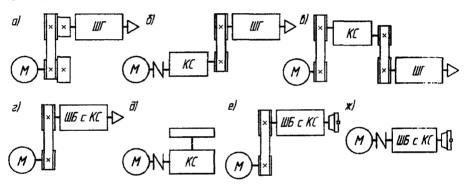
Рисунок I — Типовые структуры главного привода станков с ЧПУ: ШБ – шпиндельная бабка; КС – коробка скоростей; ШГ – шпиндельная головка
